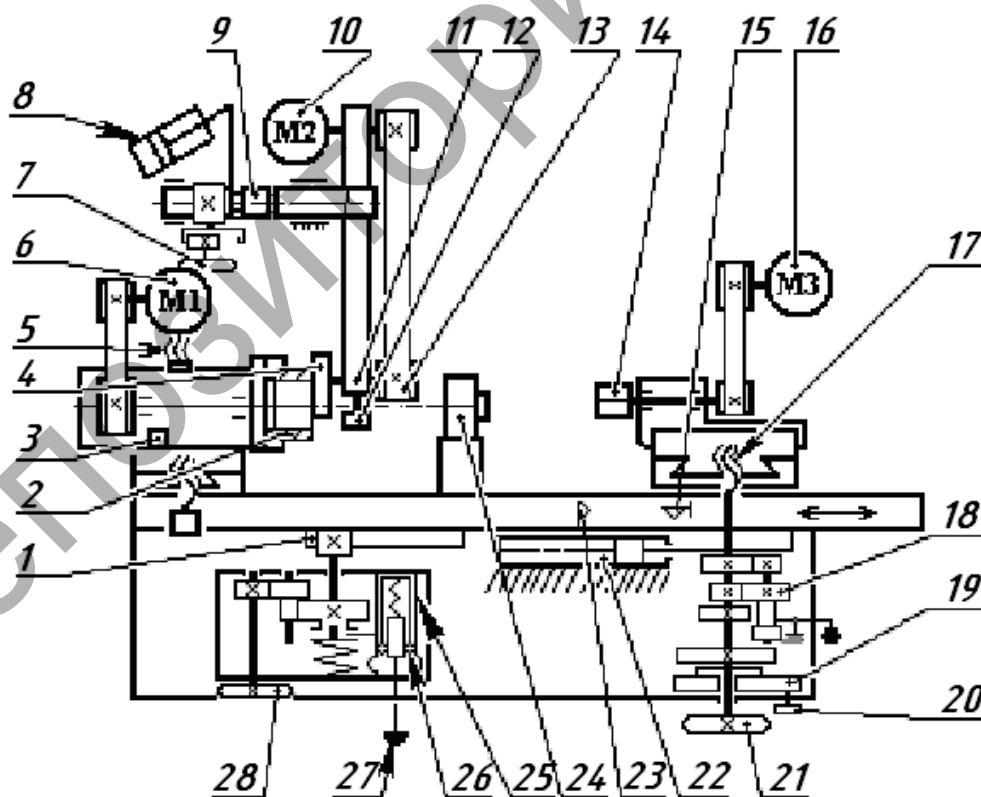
Кинематическая схема универсального внутришлифовального станка модели 3К227В
